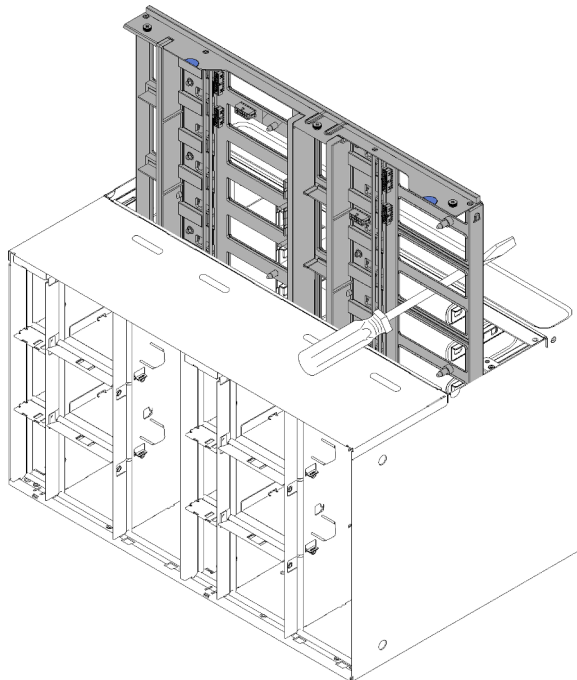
Entfernen der Mittelplatte des Gehäuses aus einem Gehäuse
